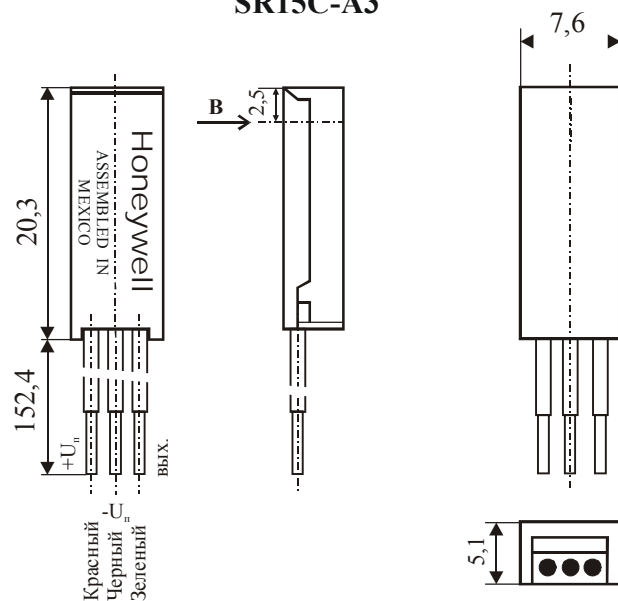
Внешний вид и габаритные размеры датчиков приближения типа SR15C-A3
